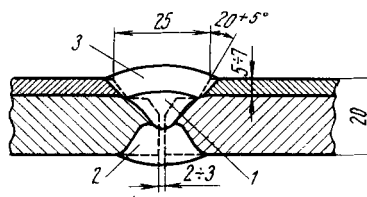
Форма разделки и схема сварки двуслойного проката Ст. 3 и X18H10T
